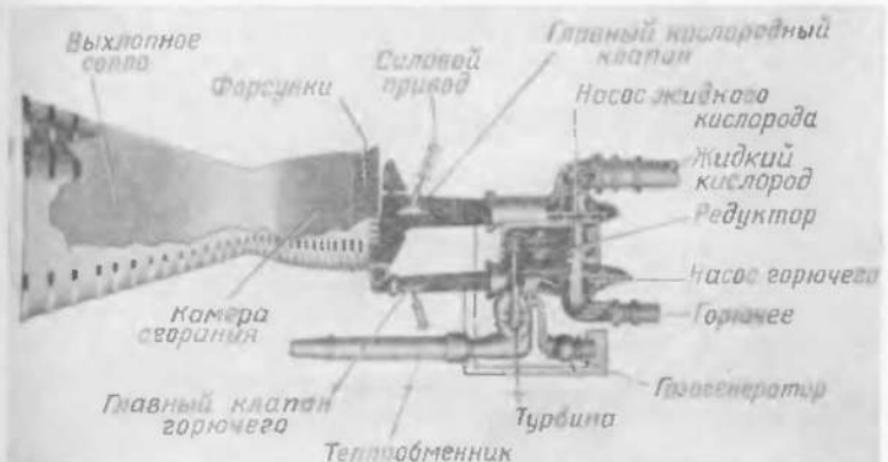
Типовой жидкостный ракетный двигатель для баллистической ракеты:
